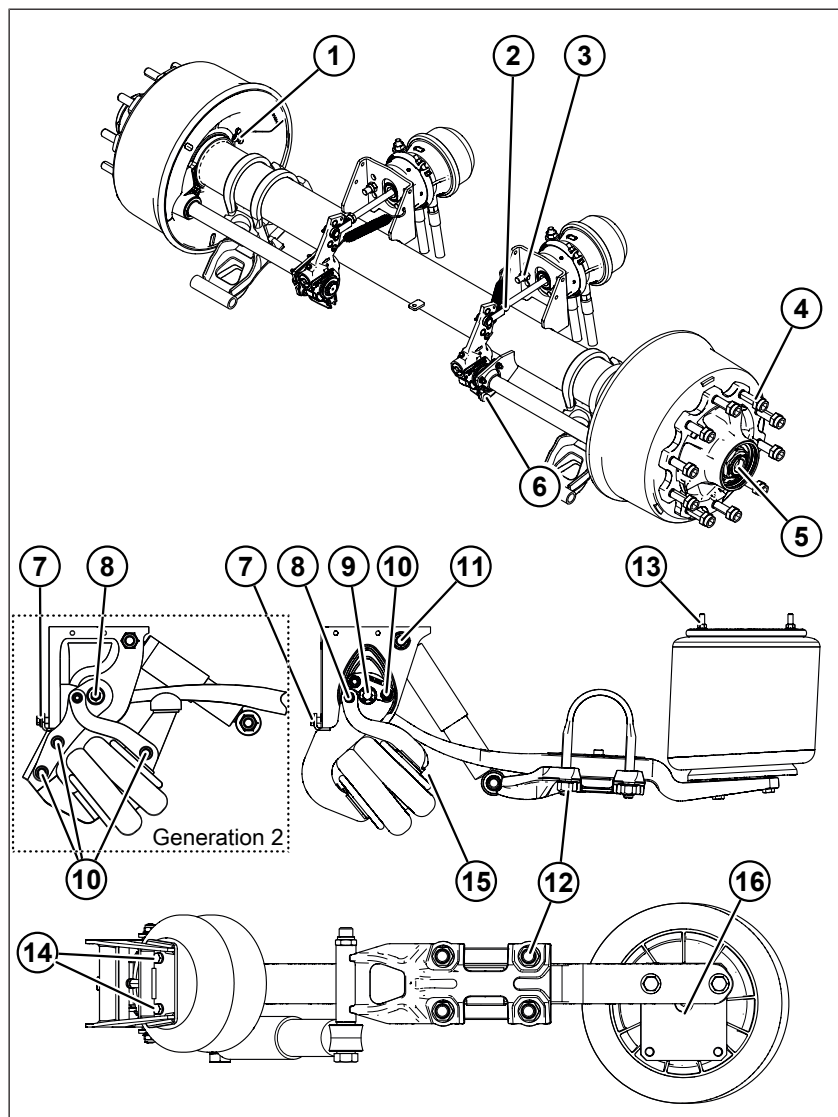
Vue d'ensemble des couples de contrôle et de serrage (bras de suspension pneumatique inférieur)
